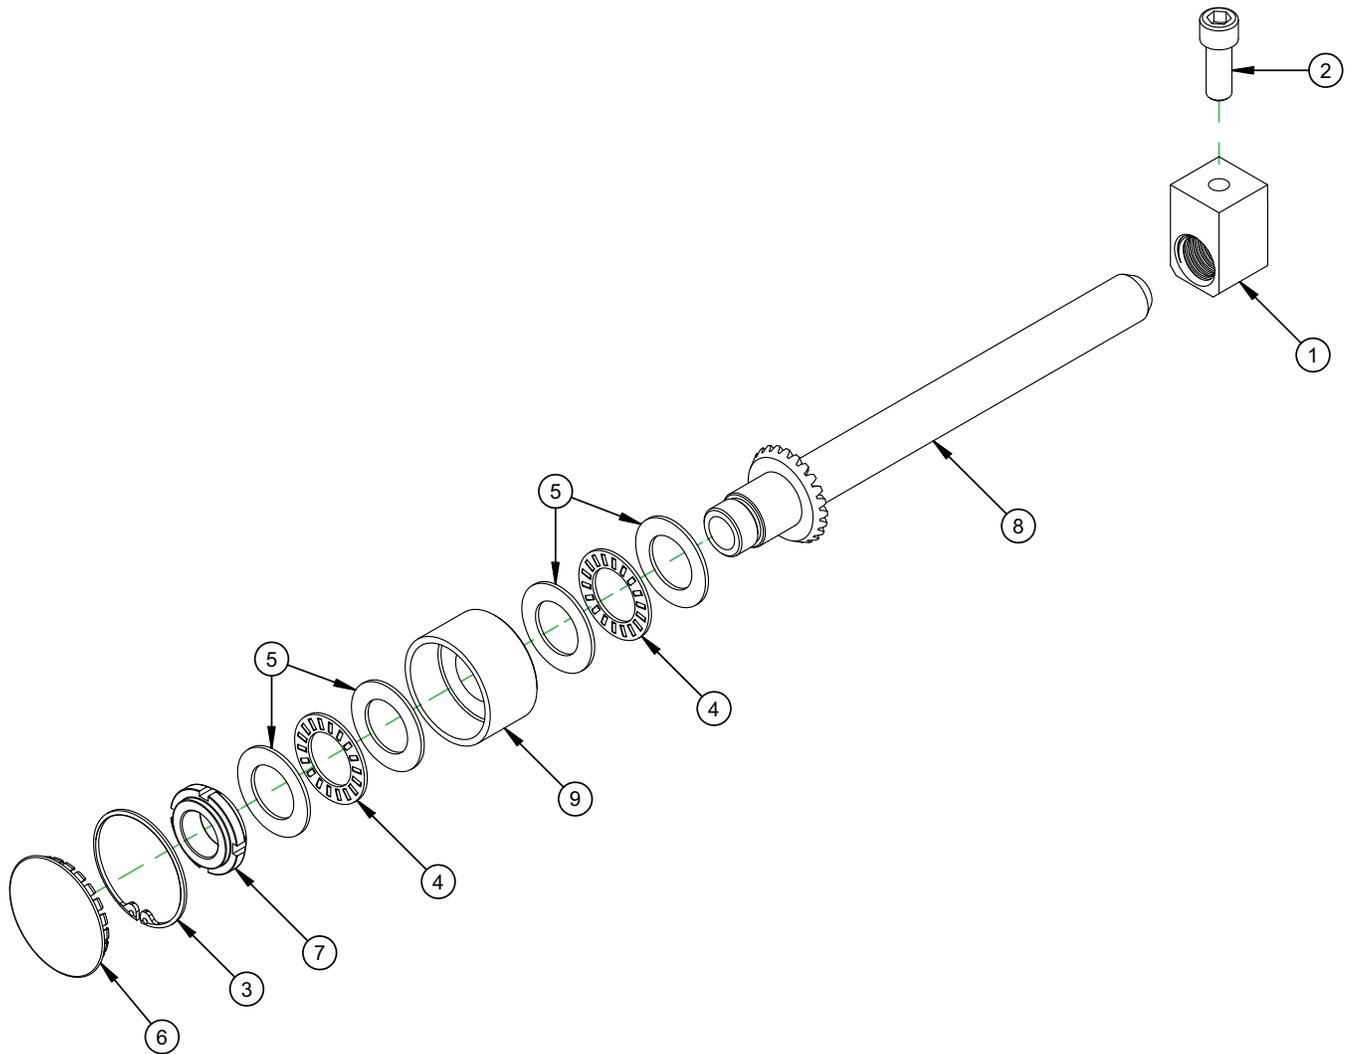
ENSEMBLE DE SERRAGE (RÉF. 15647)
